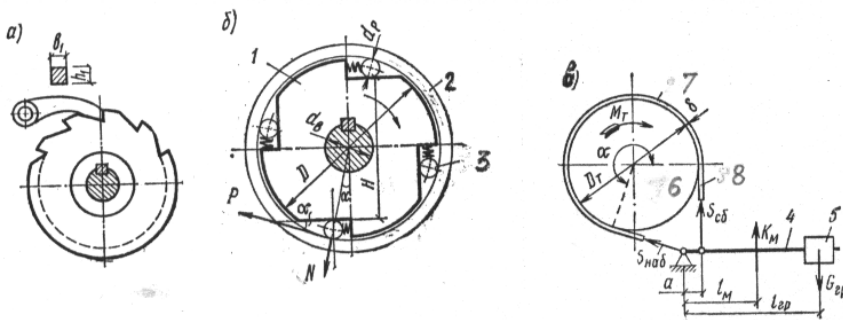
Схемы останова и ленточного тормоза: а – храповый останов; б – роликовый останов; в – простой ленточный тормоз; 1 – храповый диск; 2 – неподвижное наружное кольцо; 3 – ролики; 4 – рычаг; 5 – тормозной груз; 6 – шкив; 7 – стальная лента; 8 – тормозная накладка
